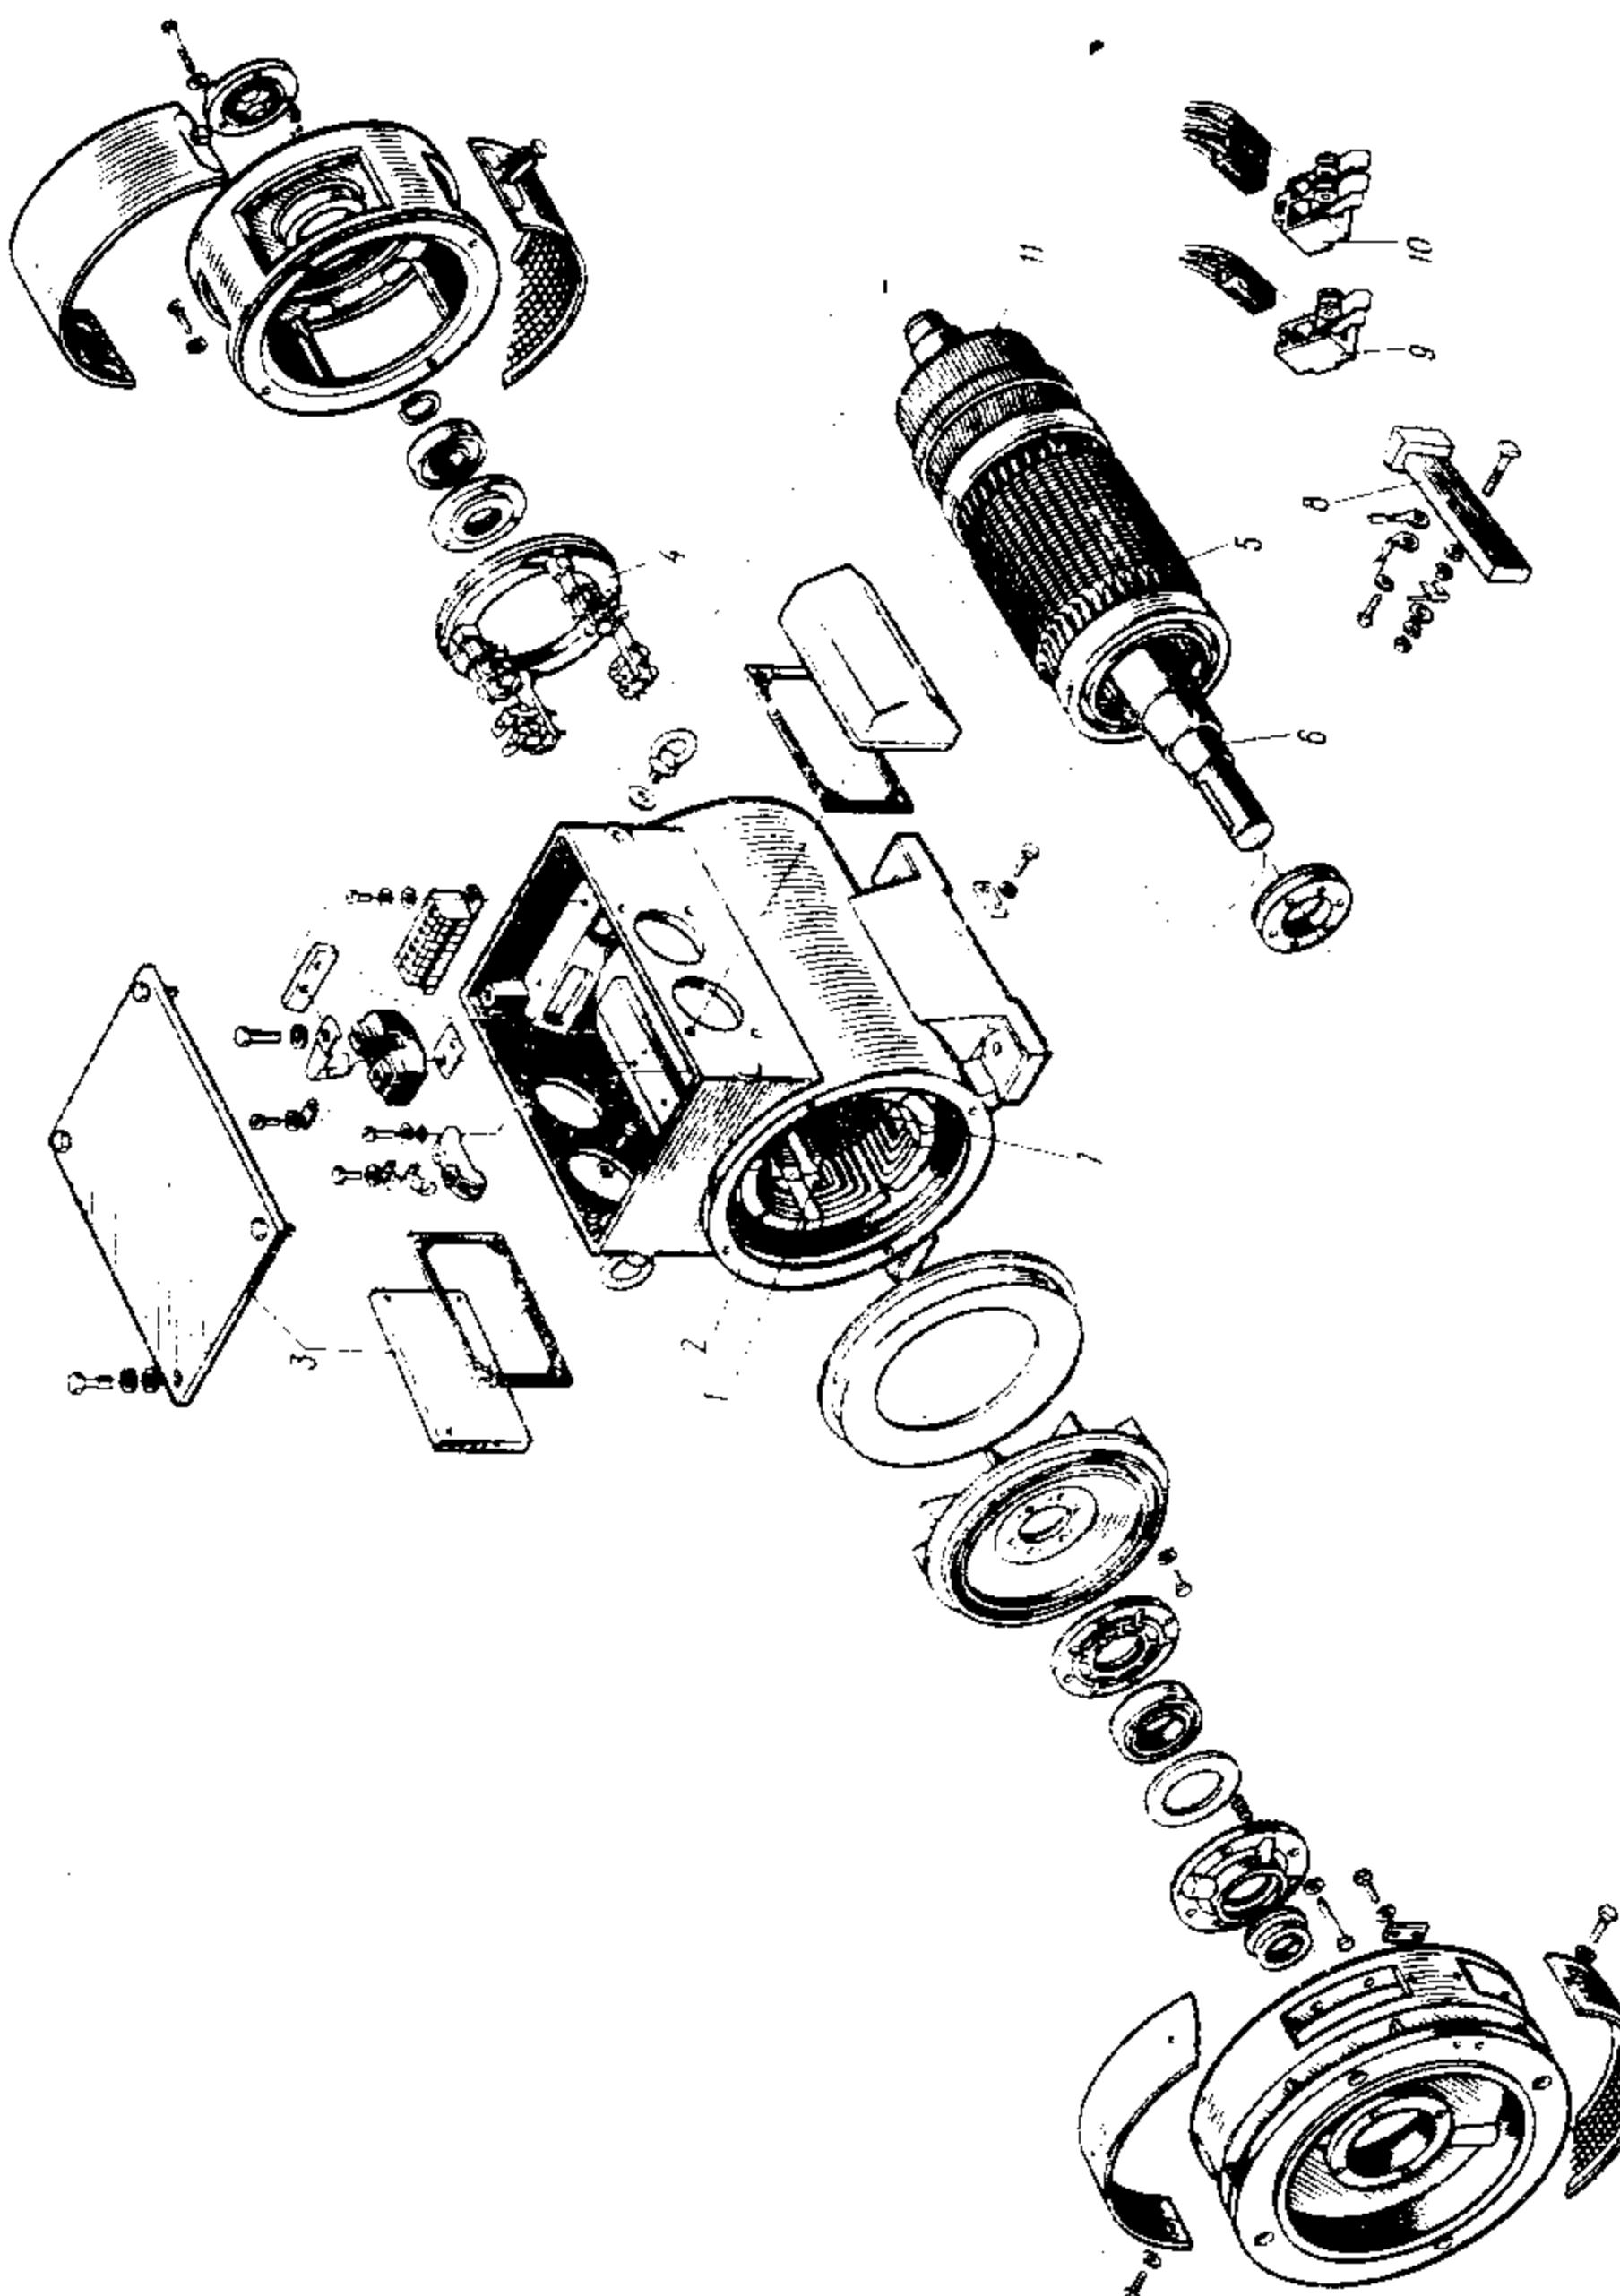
Устройство двигателя постоянного тока для привода главного движения
